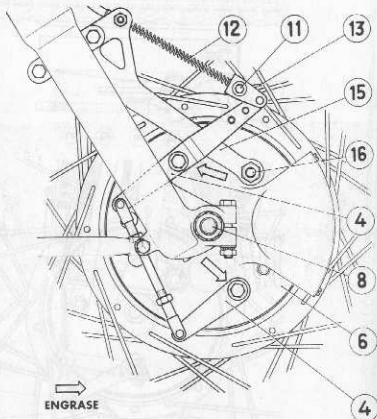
Freno delantero: Reglaje, recuperación desgaste y engrase.
